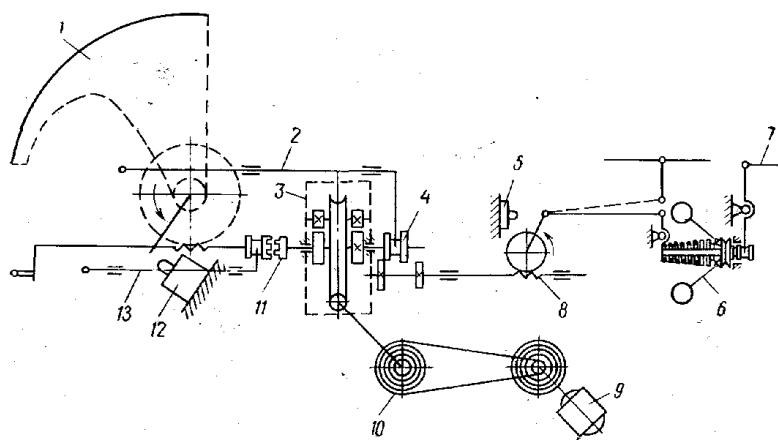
Кинематическая схема установки для автоматической приработки
